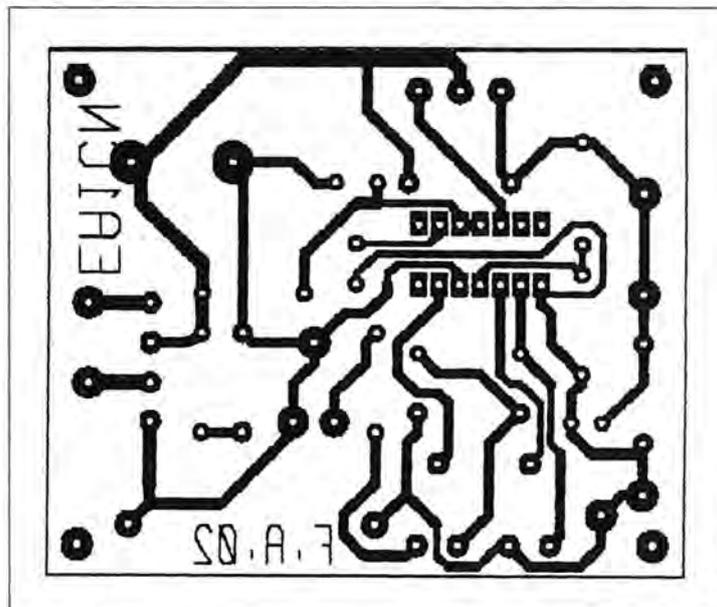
Placa de circuito impreso, vista por la cara de componentes.
